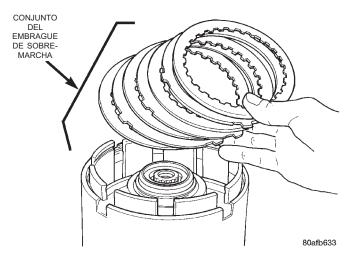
Instalación del conjunto del embrague de sobremarcha
